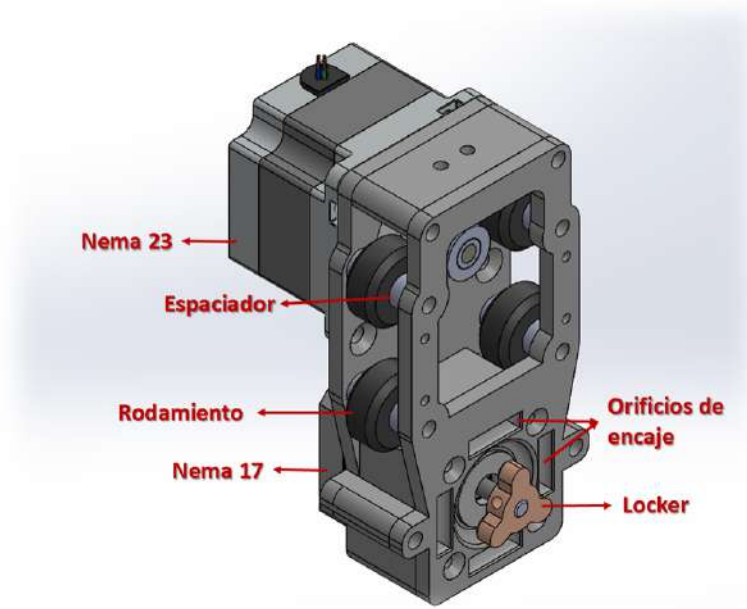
Ensamblaje CAD del carro deslizador del eje X que tiene integrado el sistema de intercambio de herramienta.
